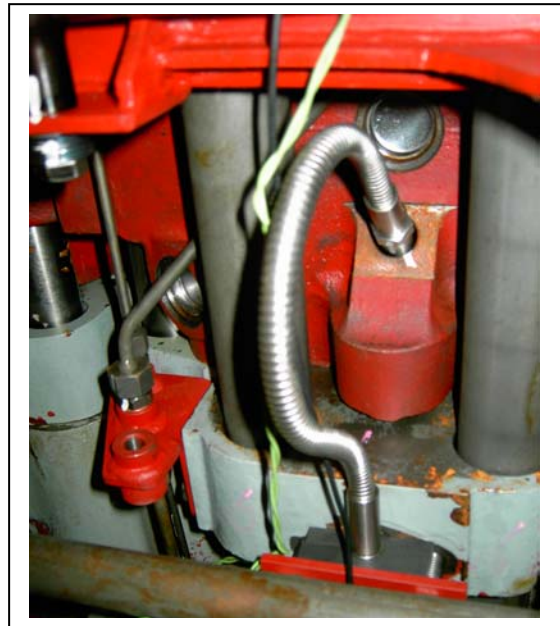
Einbauort eines IMES Zylinderdrucksensors an einem Gasmotor
